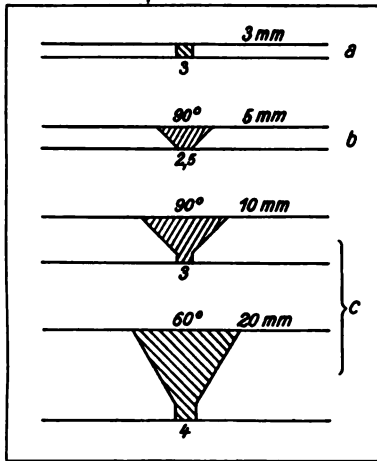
Beispiele normaler Blechschweißungen.
